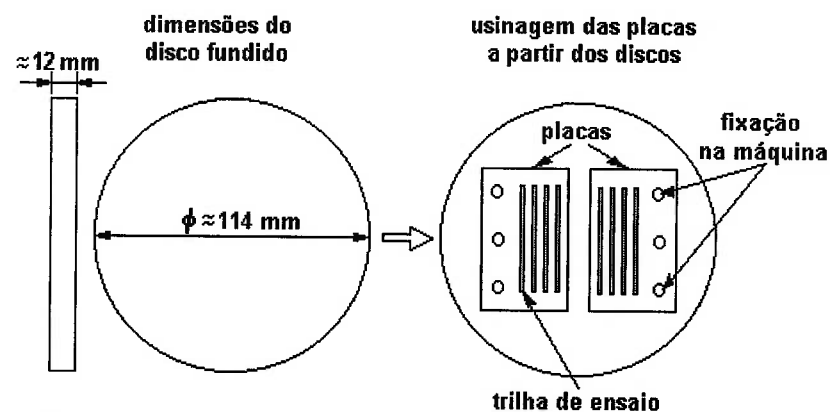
6: Esquema com dimensões do disco fundido e usinagem das placas a partir do disco.
